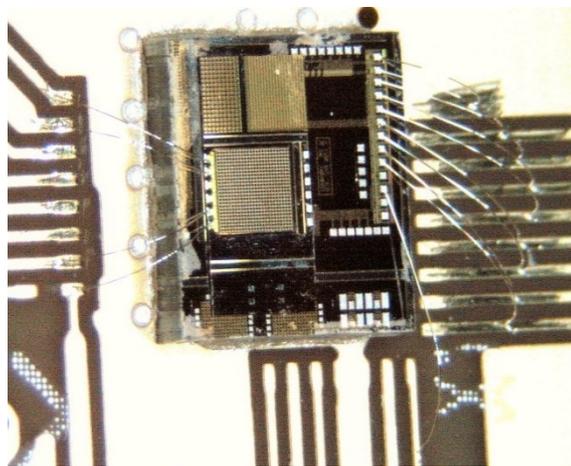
Puce PAMP/Lecture assemblée collée sur PCB de test et soudée par micropontage
